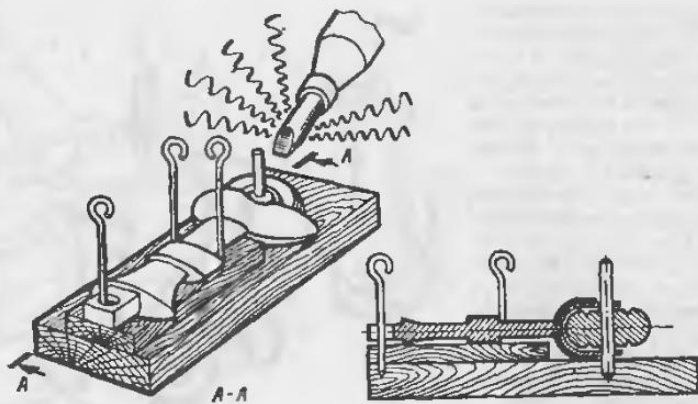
Приспособление для сборки (пайки) стойки шасси истребителя Фоккер D-21 (Голландия)
